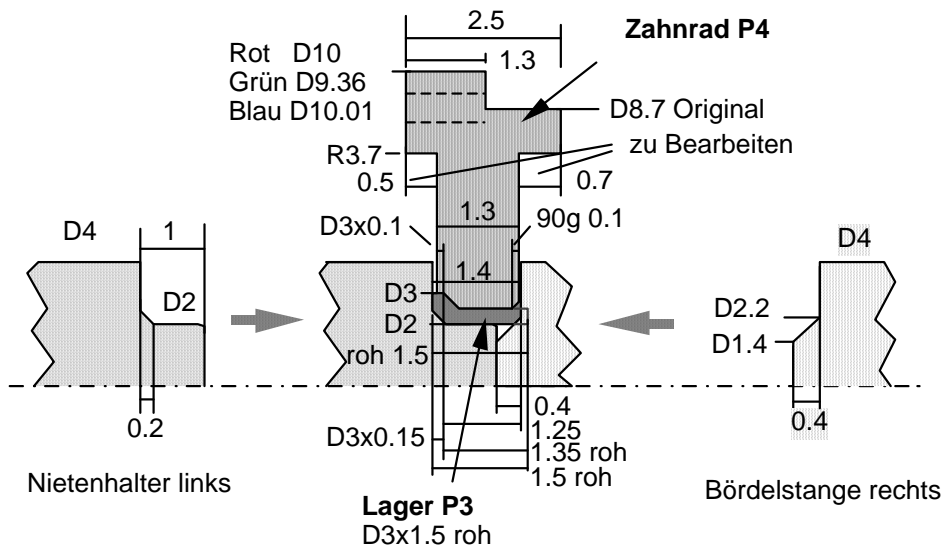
Detail Laufbüchse mit Bördelwerkzeug
